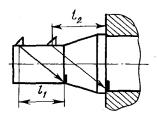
Схема контролирования цилиндроконической оси с подшипниками скольжения
